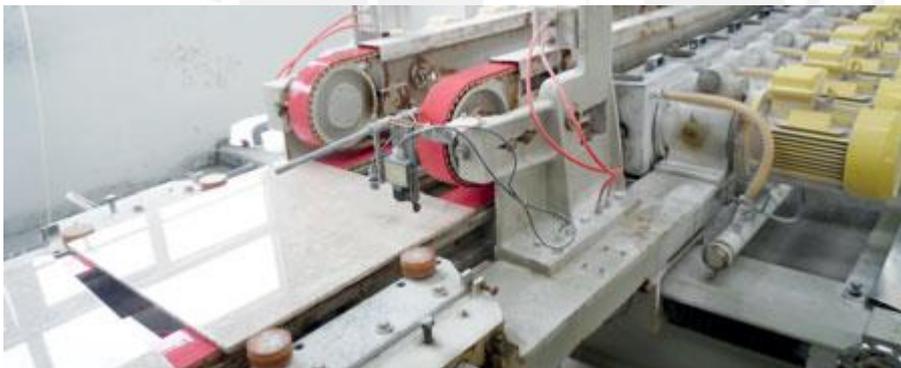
Cerámico cortado por un mecanismo automático. Imagen recuperada de Building and Construction Authority (2010)
